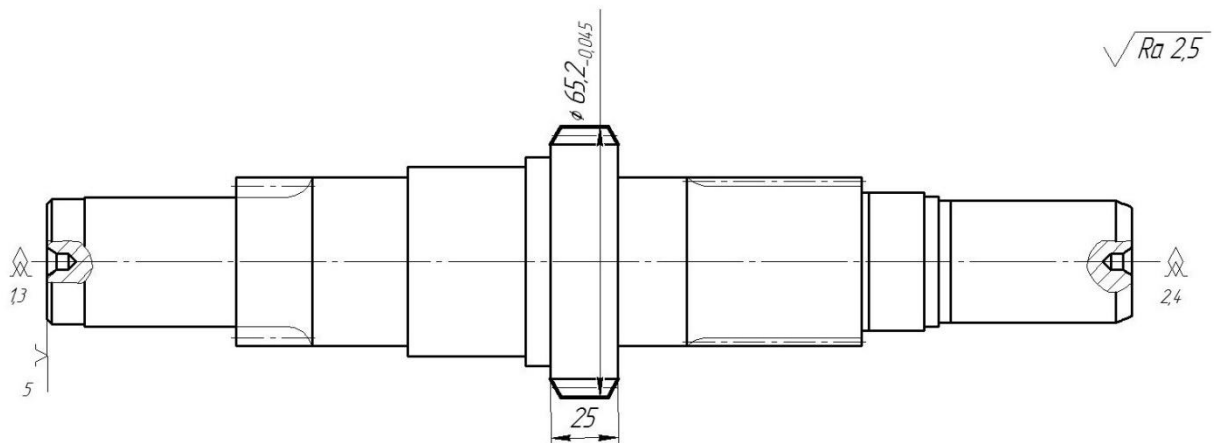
Схема процесу фрезерування вторинного вала коробки перемикавання передач Ford Explorer під час відновлення.
